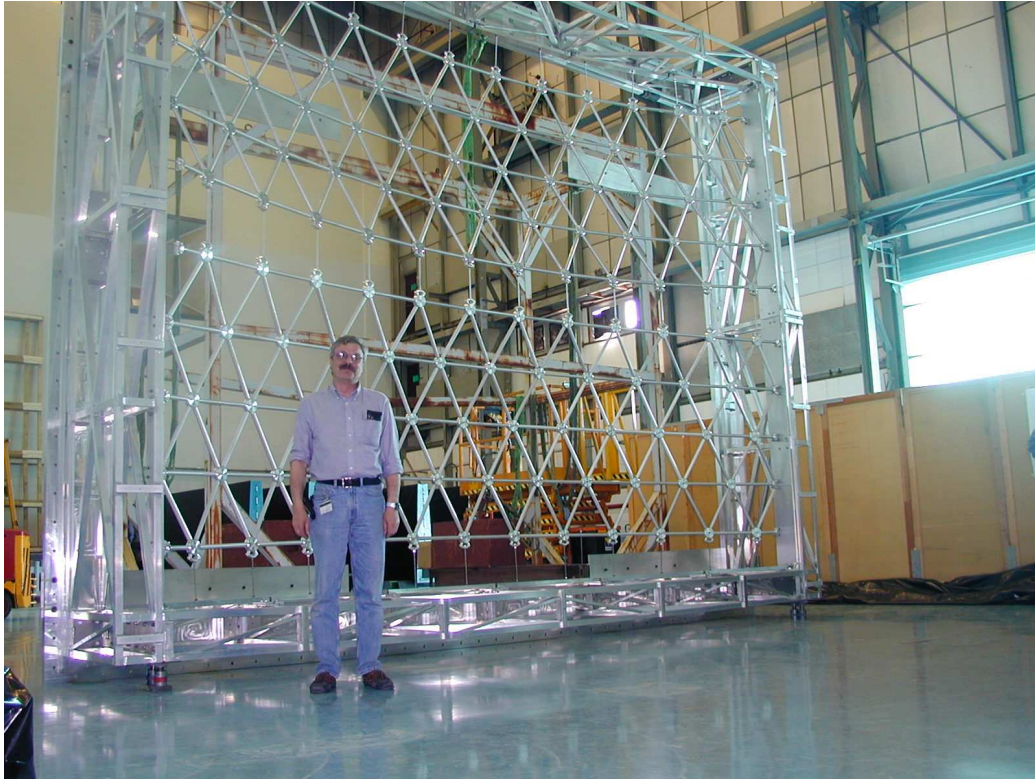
Struttura reticolare della struttura di supporto degli specchi montati.
